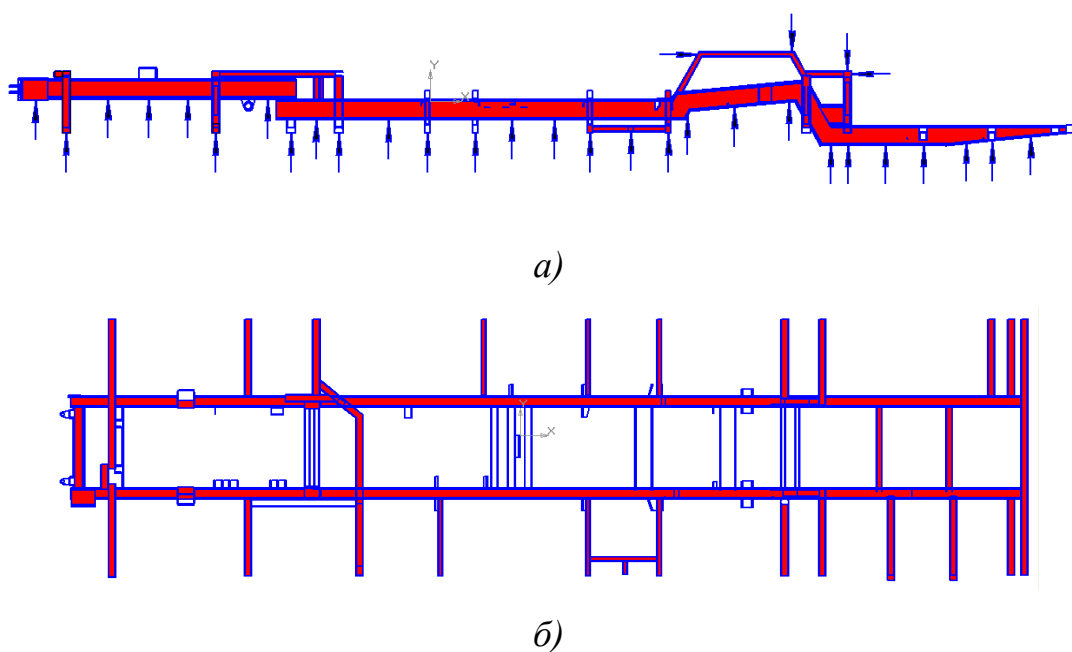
Схема обробки каркасу основи кузова автобуса: *а)* – вид збоку; *б)* – вид зверху
